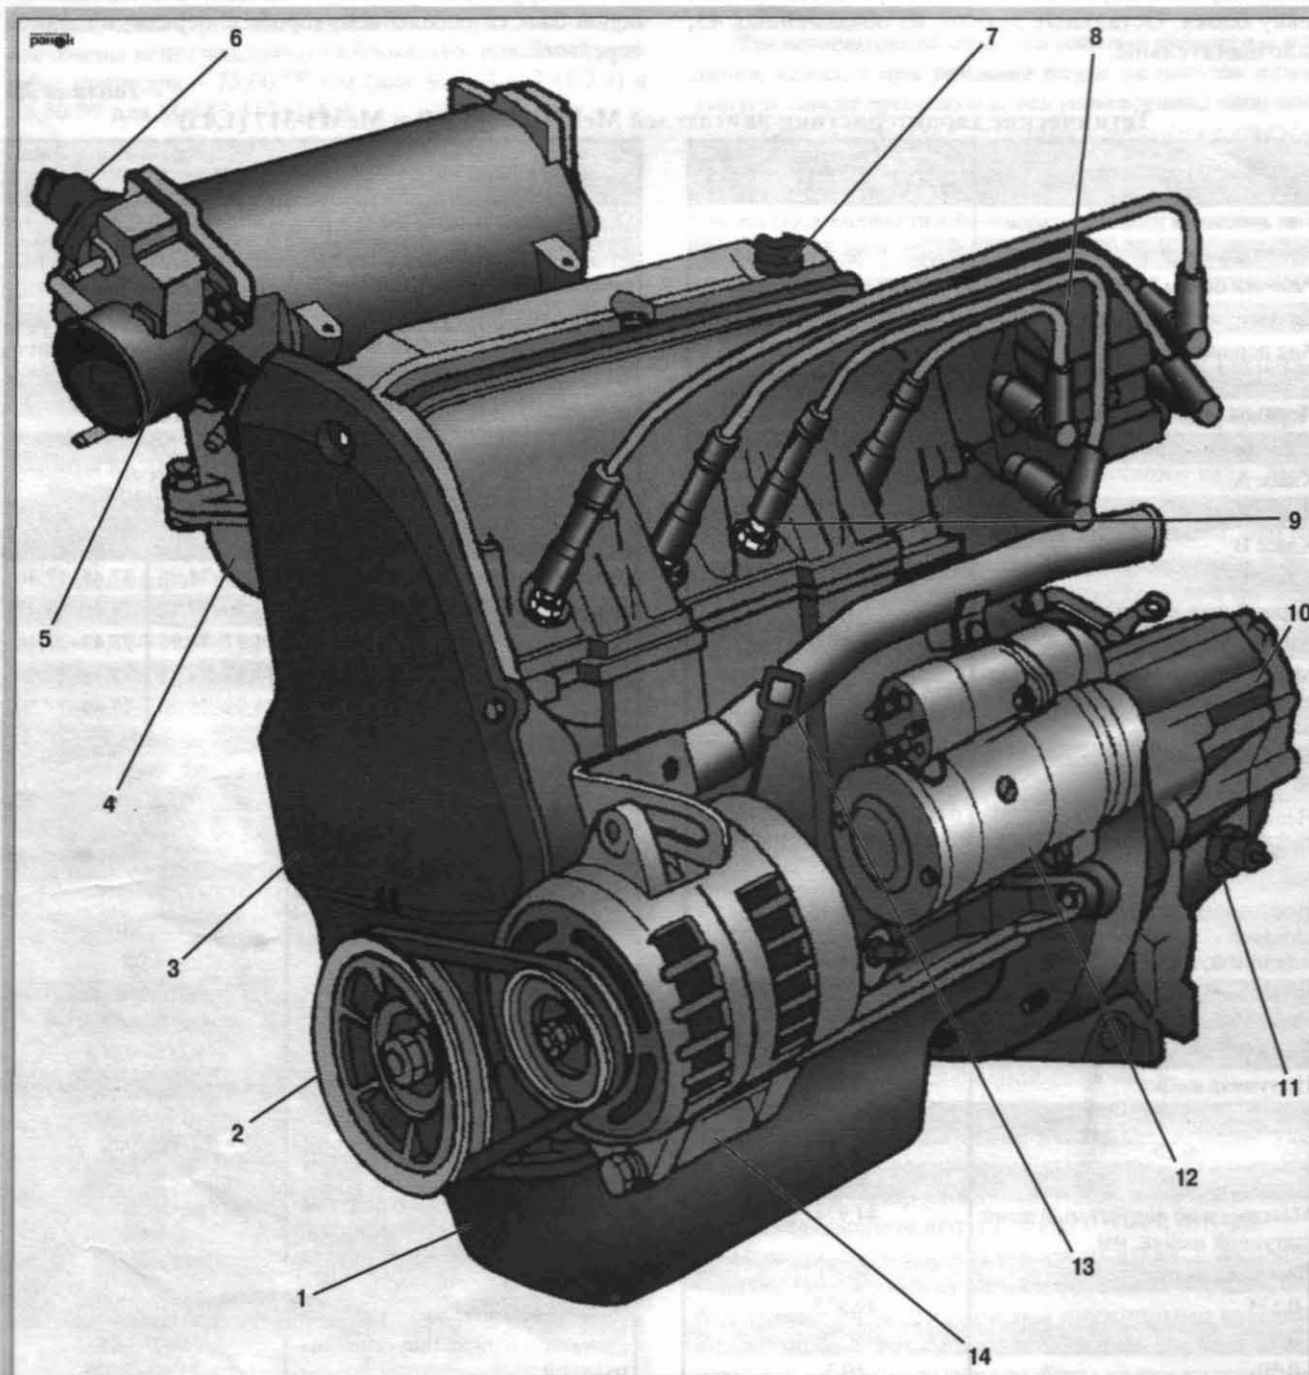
Общий вид силовых агрегатов MeM3-307 (1,3 i) и MeM3-317 (1,4 i): 1 – крышка масляного картера; 2 – шкив привода генератора; 3 – защитная крышка; 4 – впускной коллектор; 5 – воздушный патрубок; 6 – регулятор холостого хода; 7 – крышка маслозаливной горловины; 8 – модуль зажигания; 9 – свеча зажигания; 10 – коробка переключения передач; 11 – датчик скорости; 12 – стартер; 13 – щуп масляный; 14 – генератор
